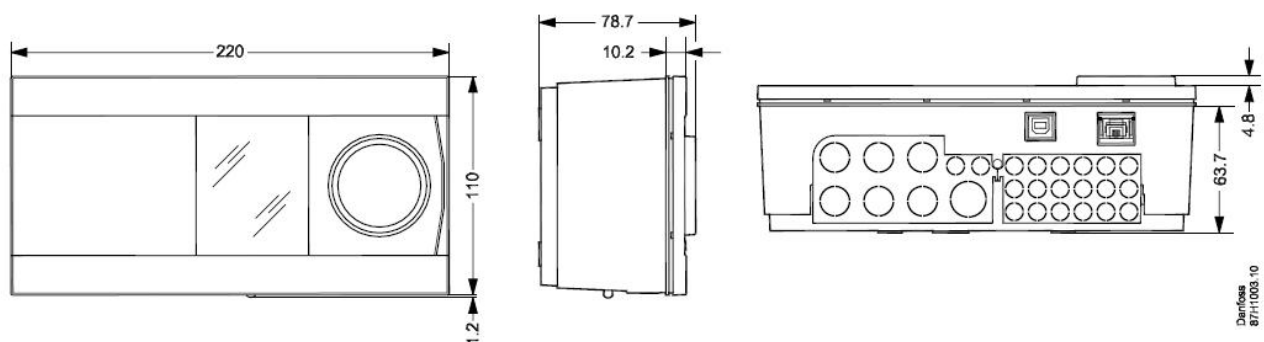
Габаритные и присоединительные размеры ECL Comfort 210.
